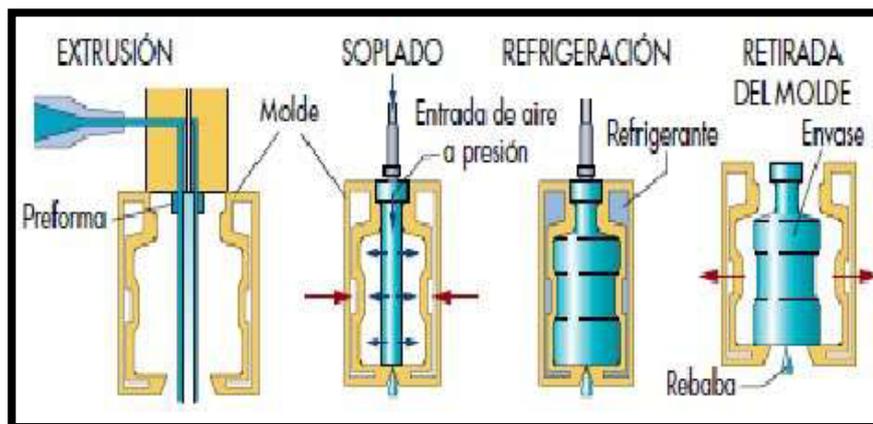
EXTRUSIÓN POR SOPLADO
